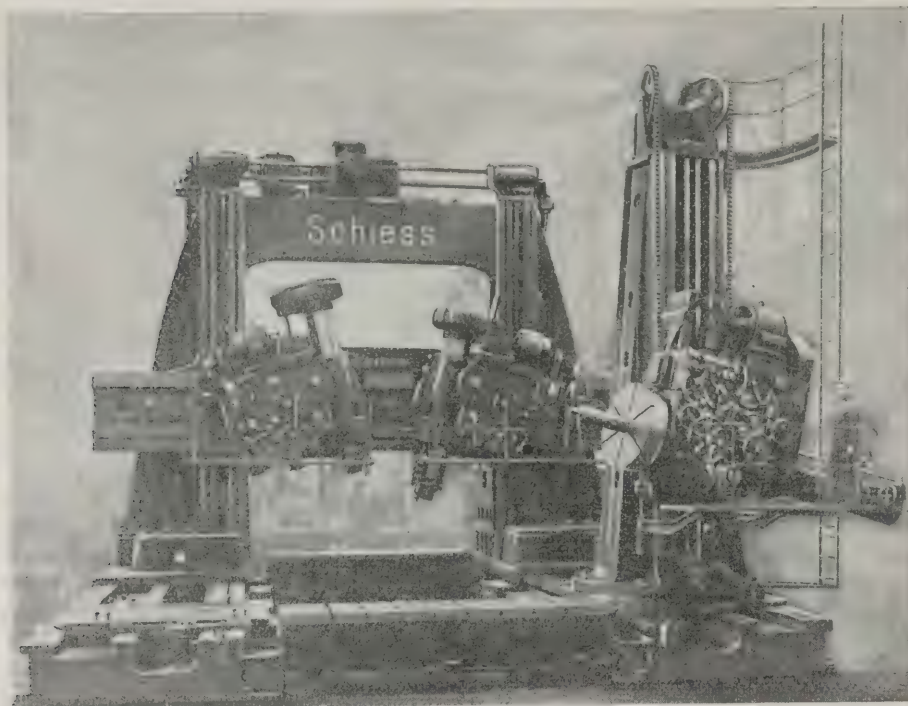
Gesamtansicht des Fräswerks auf dem Probestand. (Alle Werkzeugschlitten sind schräg gestellt).
